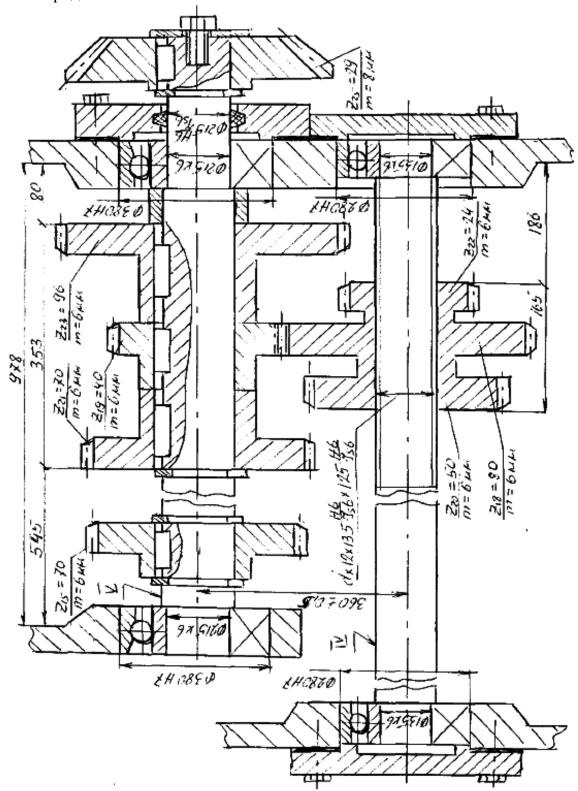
Сборочный чертеж наиболее нагруженной группы передач
